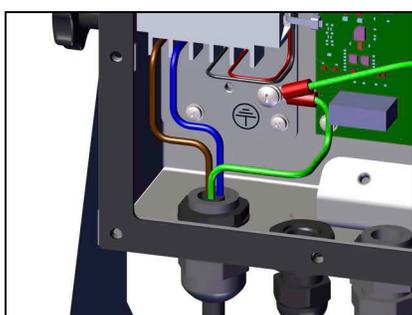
Cablaggio di alimentazione AC preinstallato
